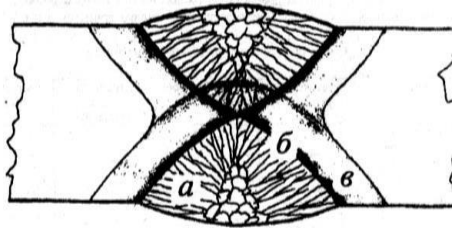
Зони зварного з'єднання: а – наплавлений метал шва (стовпчасті і рівноосні кристали); б – метал зони сплавлення; в – зона термічного впливу (зона теплового впливу)
